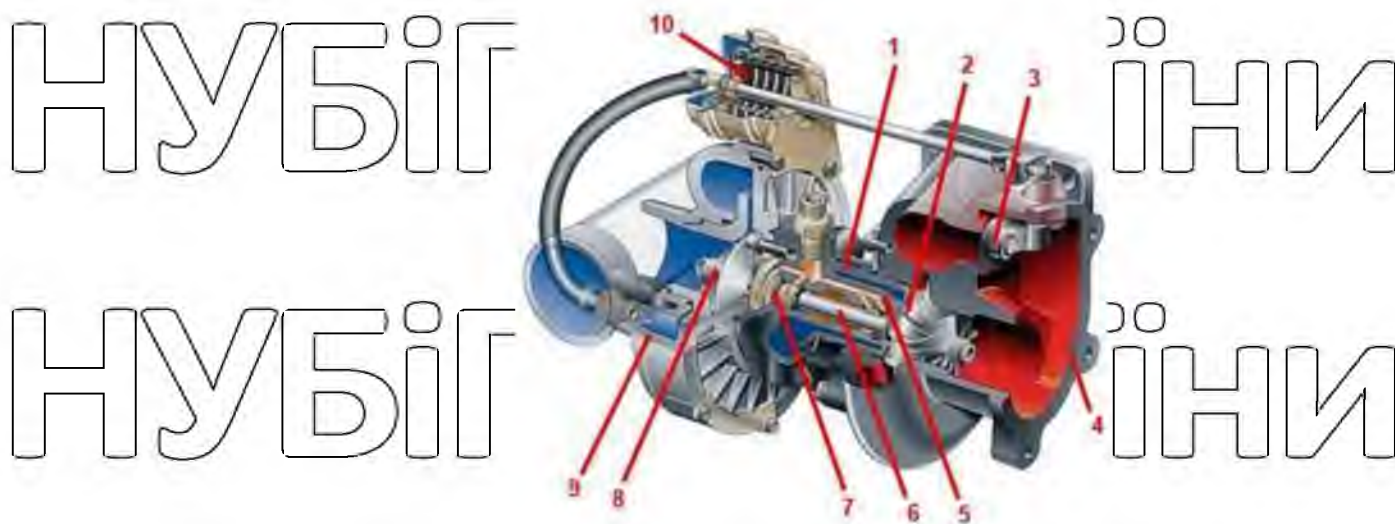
Будова сучасного компресорного устаткування: 1 - корпус підшипників; 2 - турбінне колесо; 3 - перепускний клапан; 4 - корпус турбіни; 5 - масляні канали; 6 - вал ротора; 7 - підшипник ковзання; 8 - компресорне колесо; 9 - корпус компресорного устаткування; 10 - пневмопривід перепускного клапана.
